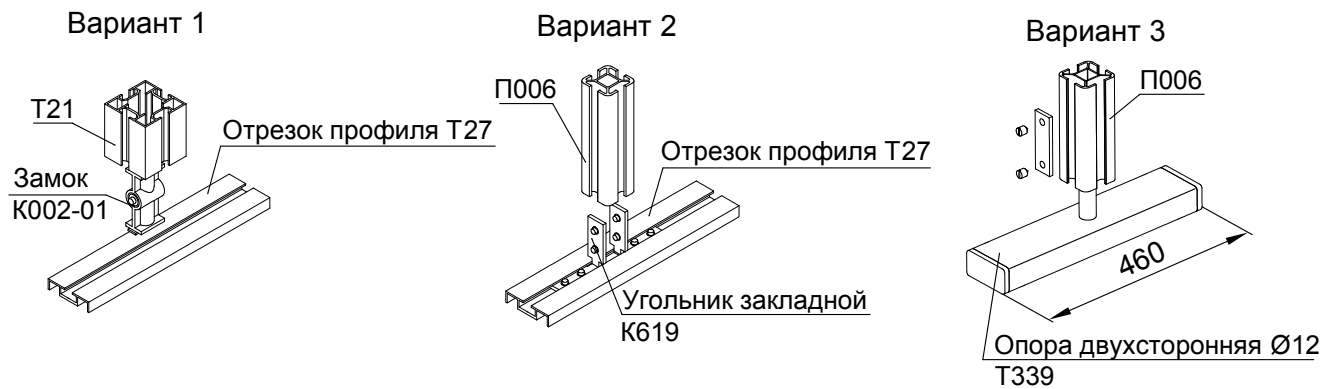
Перегородка на широких опорах с креплением к стене на расстоянии
